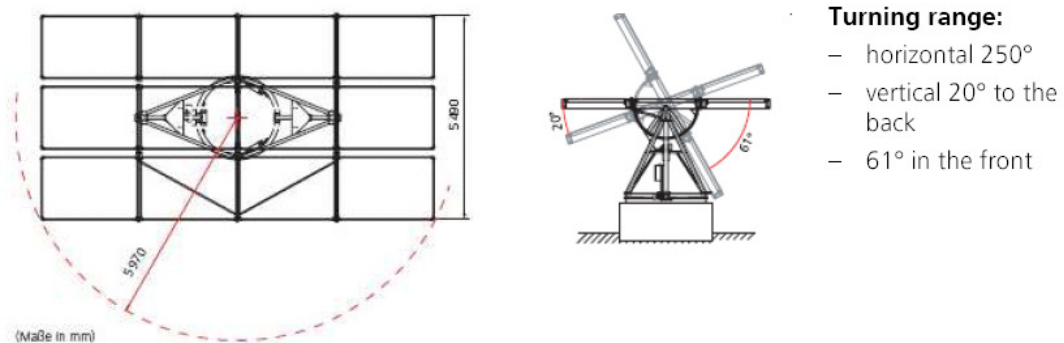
Dimensions i límits físics del model de seguidor SOLON MOVER.
